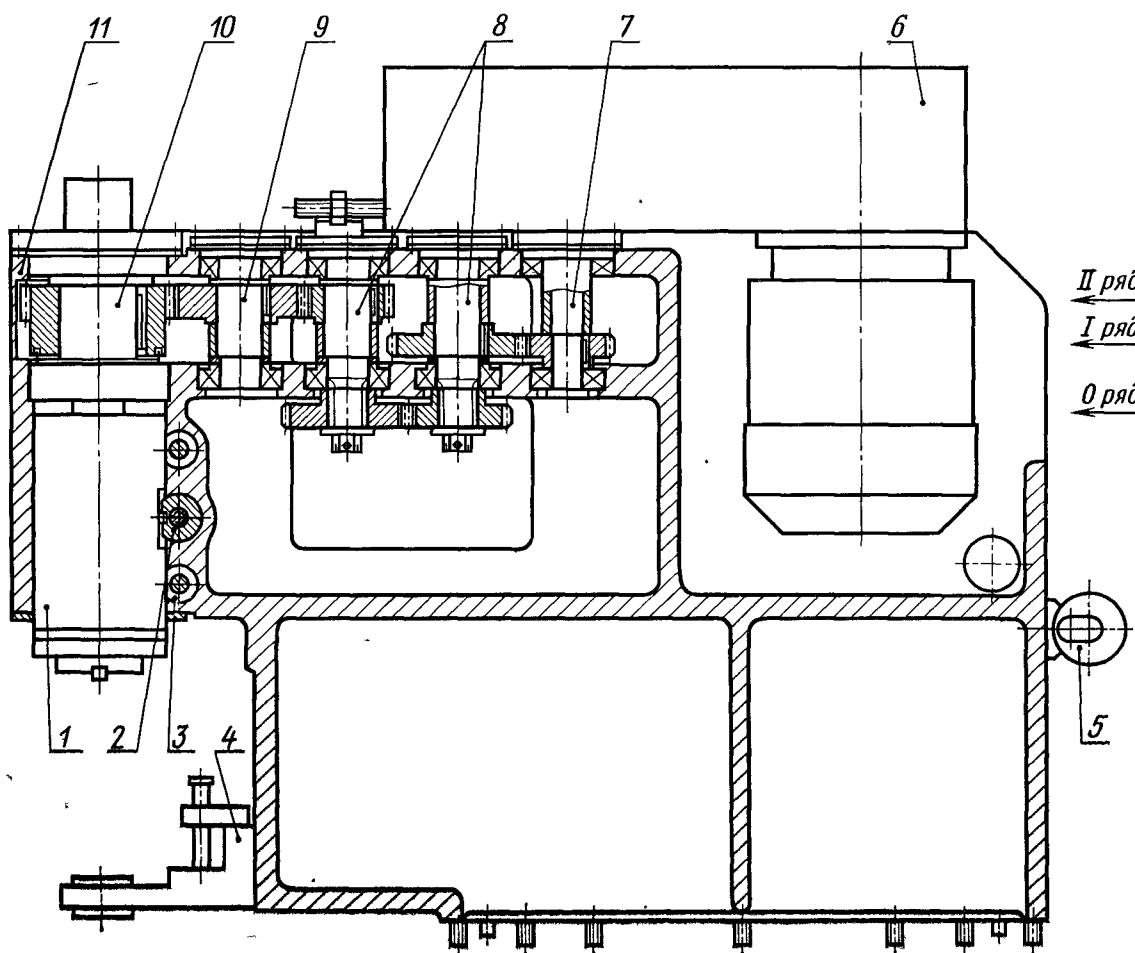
Вариант компоновки фрезерной бабки горизонтального исполнения
